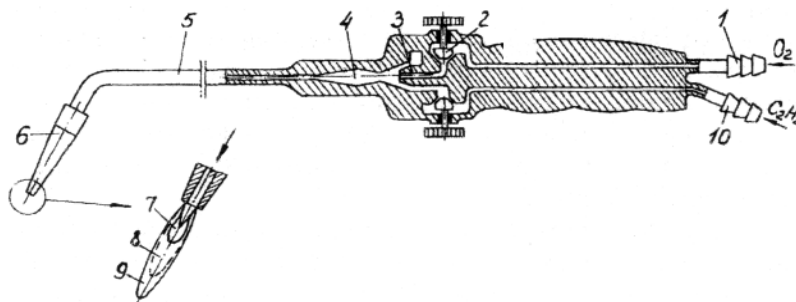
Конструктивная схема инжекторной горелки и строение сварочного пламени.
